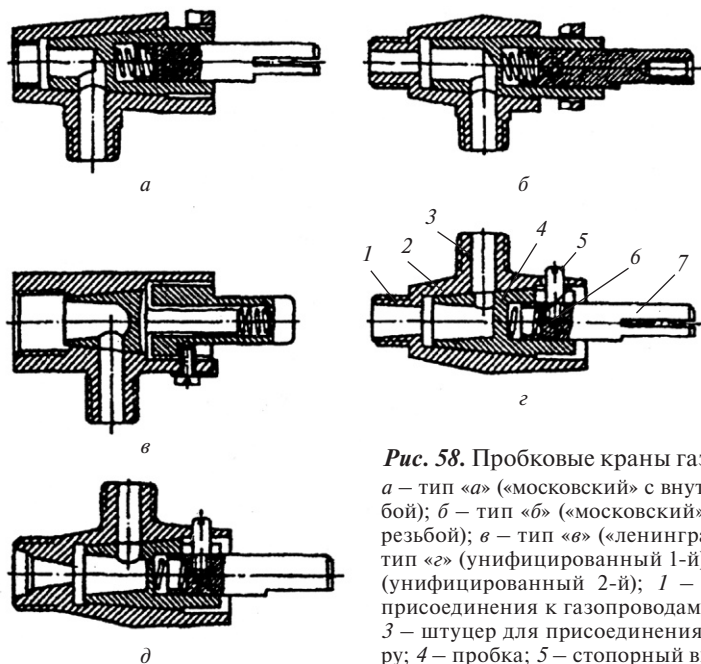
Пробковые краны газовых плит: *а* – тип «а» («московский» с внутренней резьбой); *б* – тип «б» («московский» с наружной резьбой); *в* – тип «в» («ленинградский»); *г* – тип «г» (унифицированный 1-й); *д* – тип «д» (унифицированный 2-й); 1 – штуцер для присоединения к газопроводам; 2 – корпус; 3 – штуцер для присоединения к коллектору; 4 – пробка; 5 – стопорный винт; 6 – пружина; 7 – стержень
